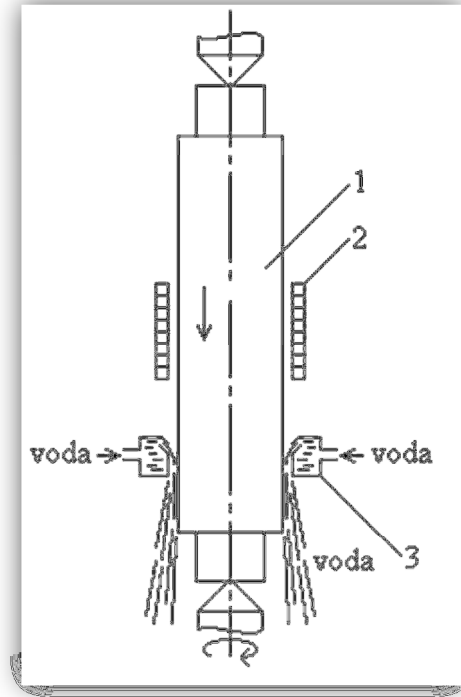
Indukční ohříváč SOR 120/20 [27]
